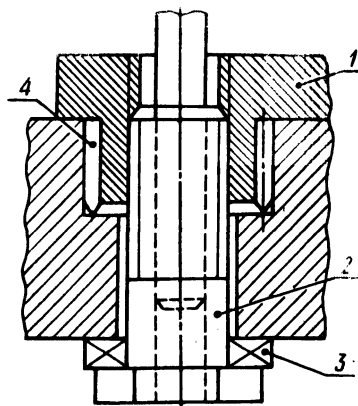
Схема модернизации трехповоротных тисков универсально-заточного станка.
